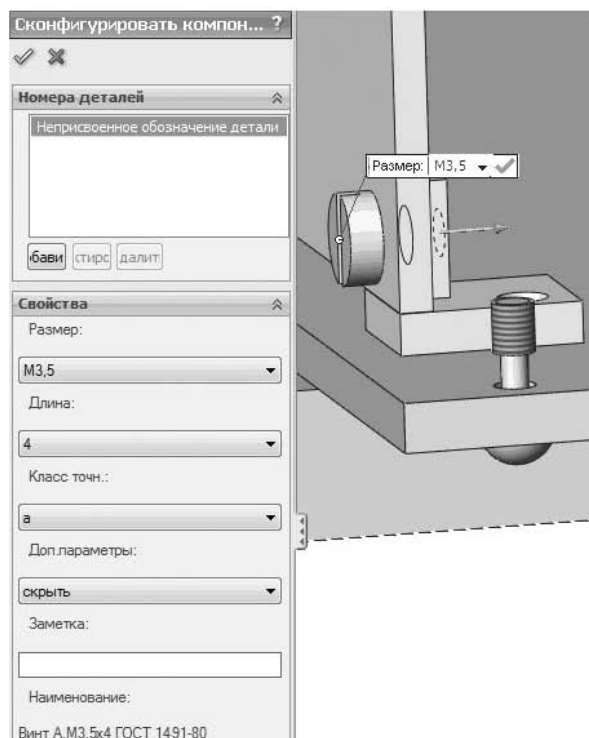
Расположение винтов для соединения уголка с печатной платой
